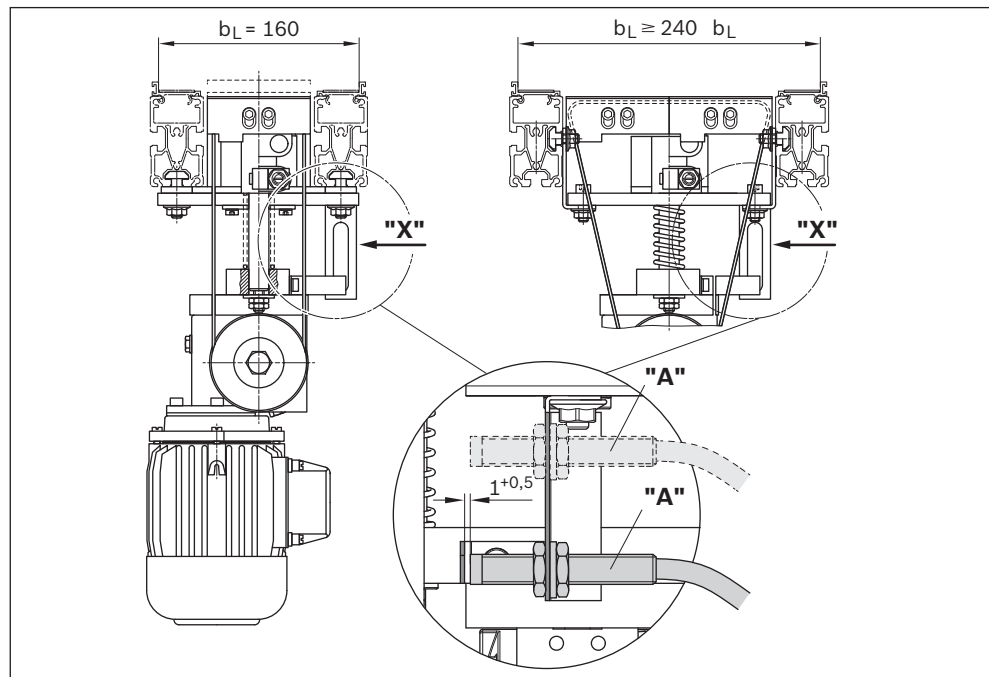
Montaggio unità di svincolo HQ 2/U, $b_L = 160$ mm
